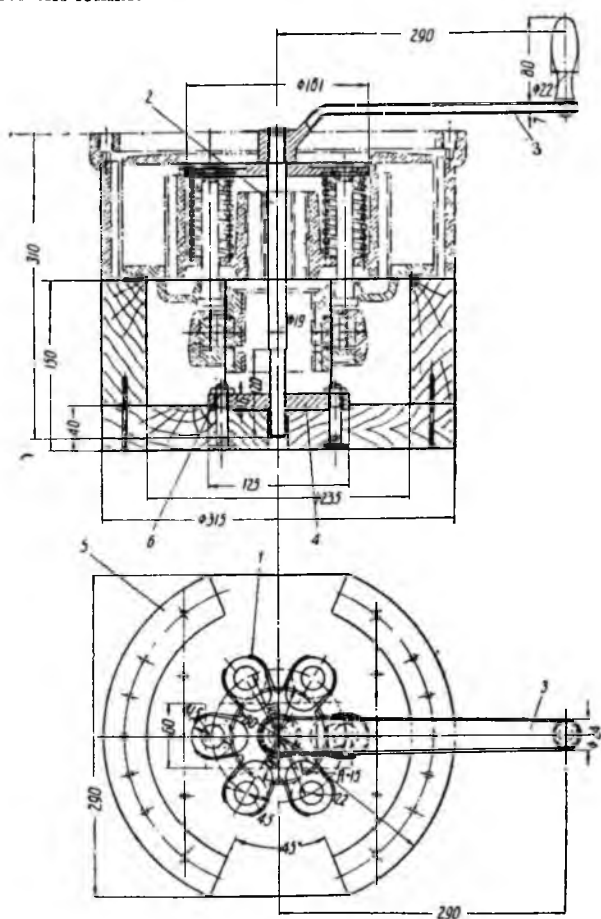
Приспособление для снятия и постановки пружин фрикционов трактора СХТЗ-НАТИ:
